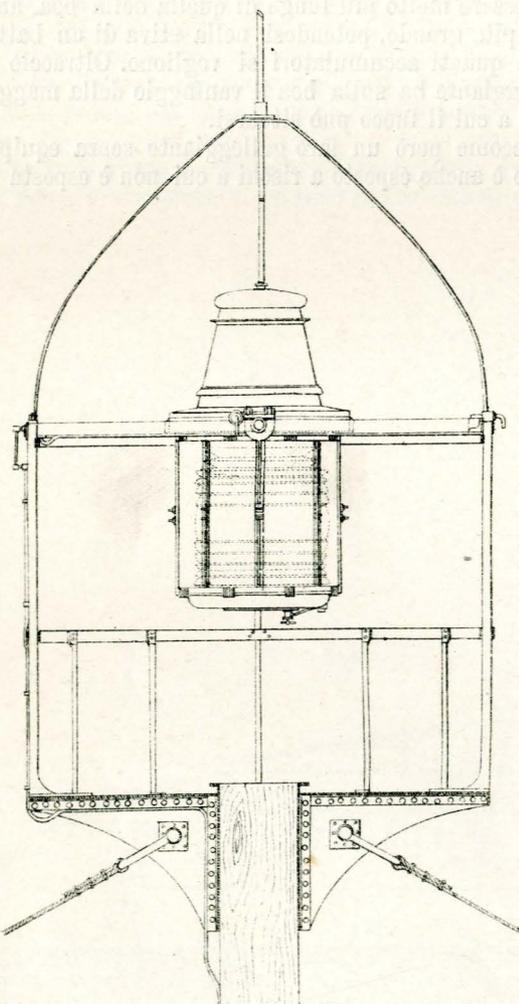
Particolarità di una lanterna Pintsch di faro galleggiante, con sospensione Cardanica.
